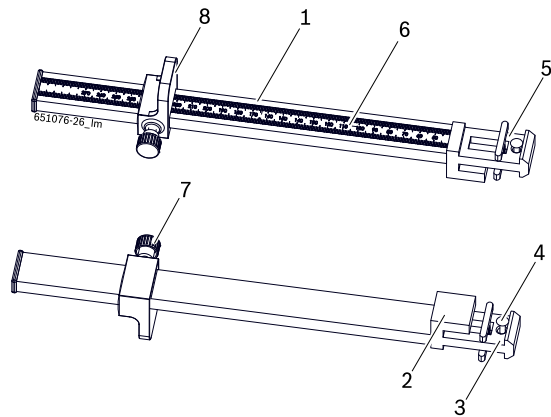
Coulisseau de mesure manuel, haut : butée réglable pour base creuse. Bas : butée fixe pour bord de jante
